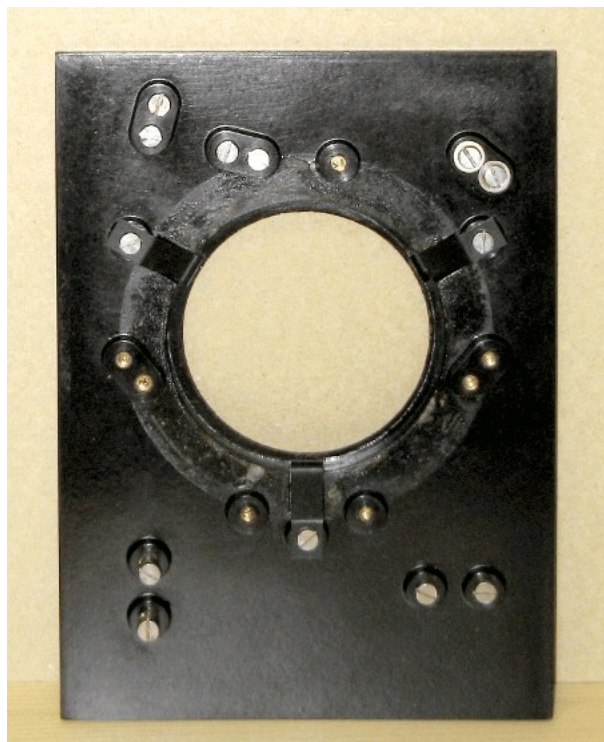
Frontplatten-Rückseite als Montageplatte. Die Schrauben sind teilweise eingedreht, um sie wegen unterschiedlicher Längen beim späteren Zusammenbau nicht zu verwechseln.
